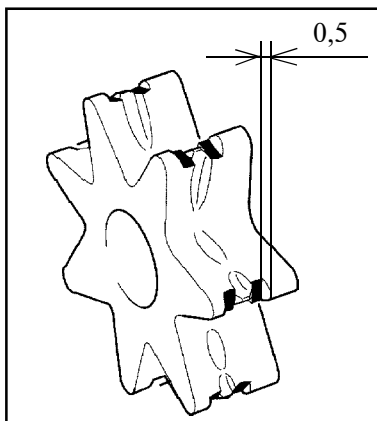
Контроль глубины выработки зуба звездочки ведущей
